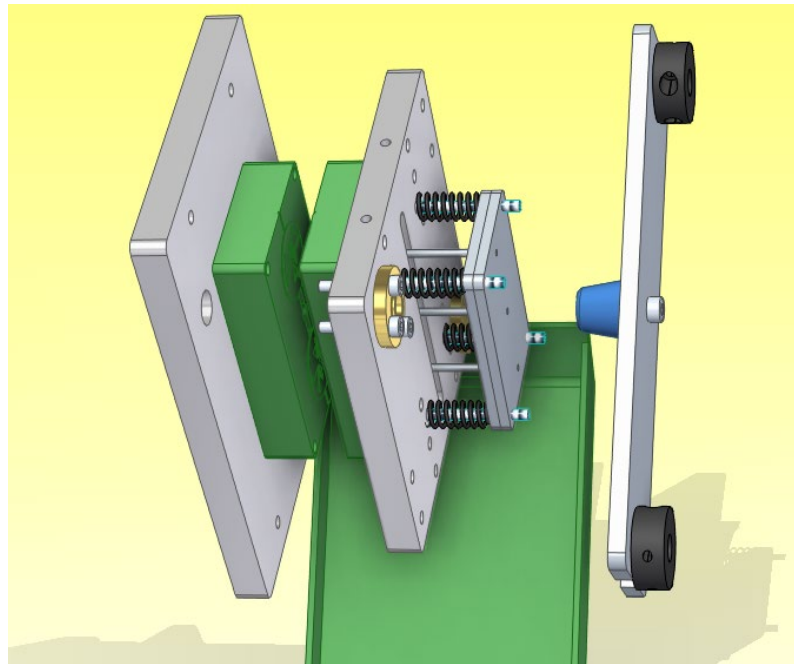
Components del subconjunt del motlle. (Font: pròpia)
